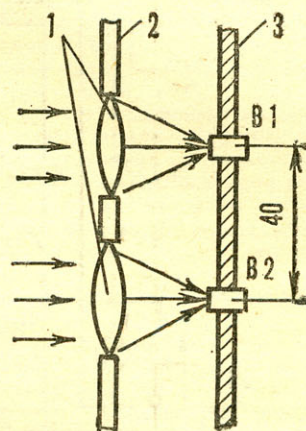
Установка дополнительных линз: 1 — линзы, 2 — крышка корпуса, 3 — монтажная плата.
